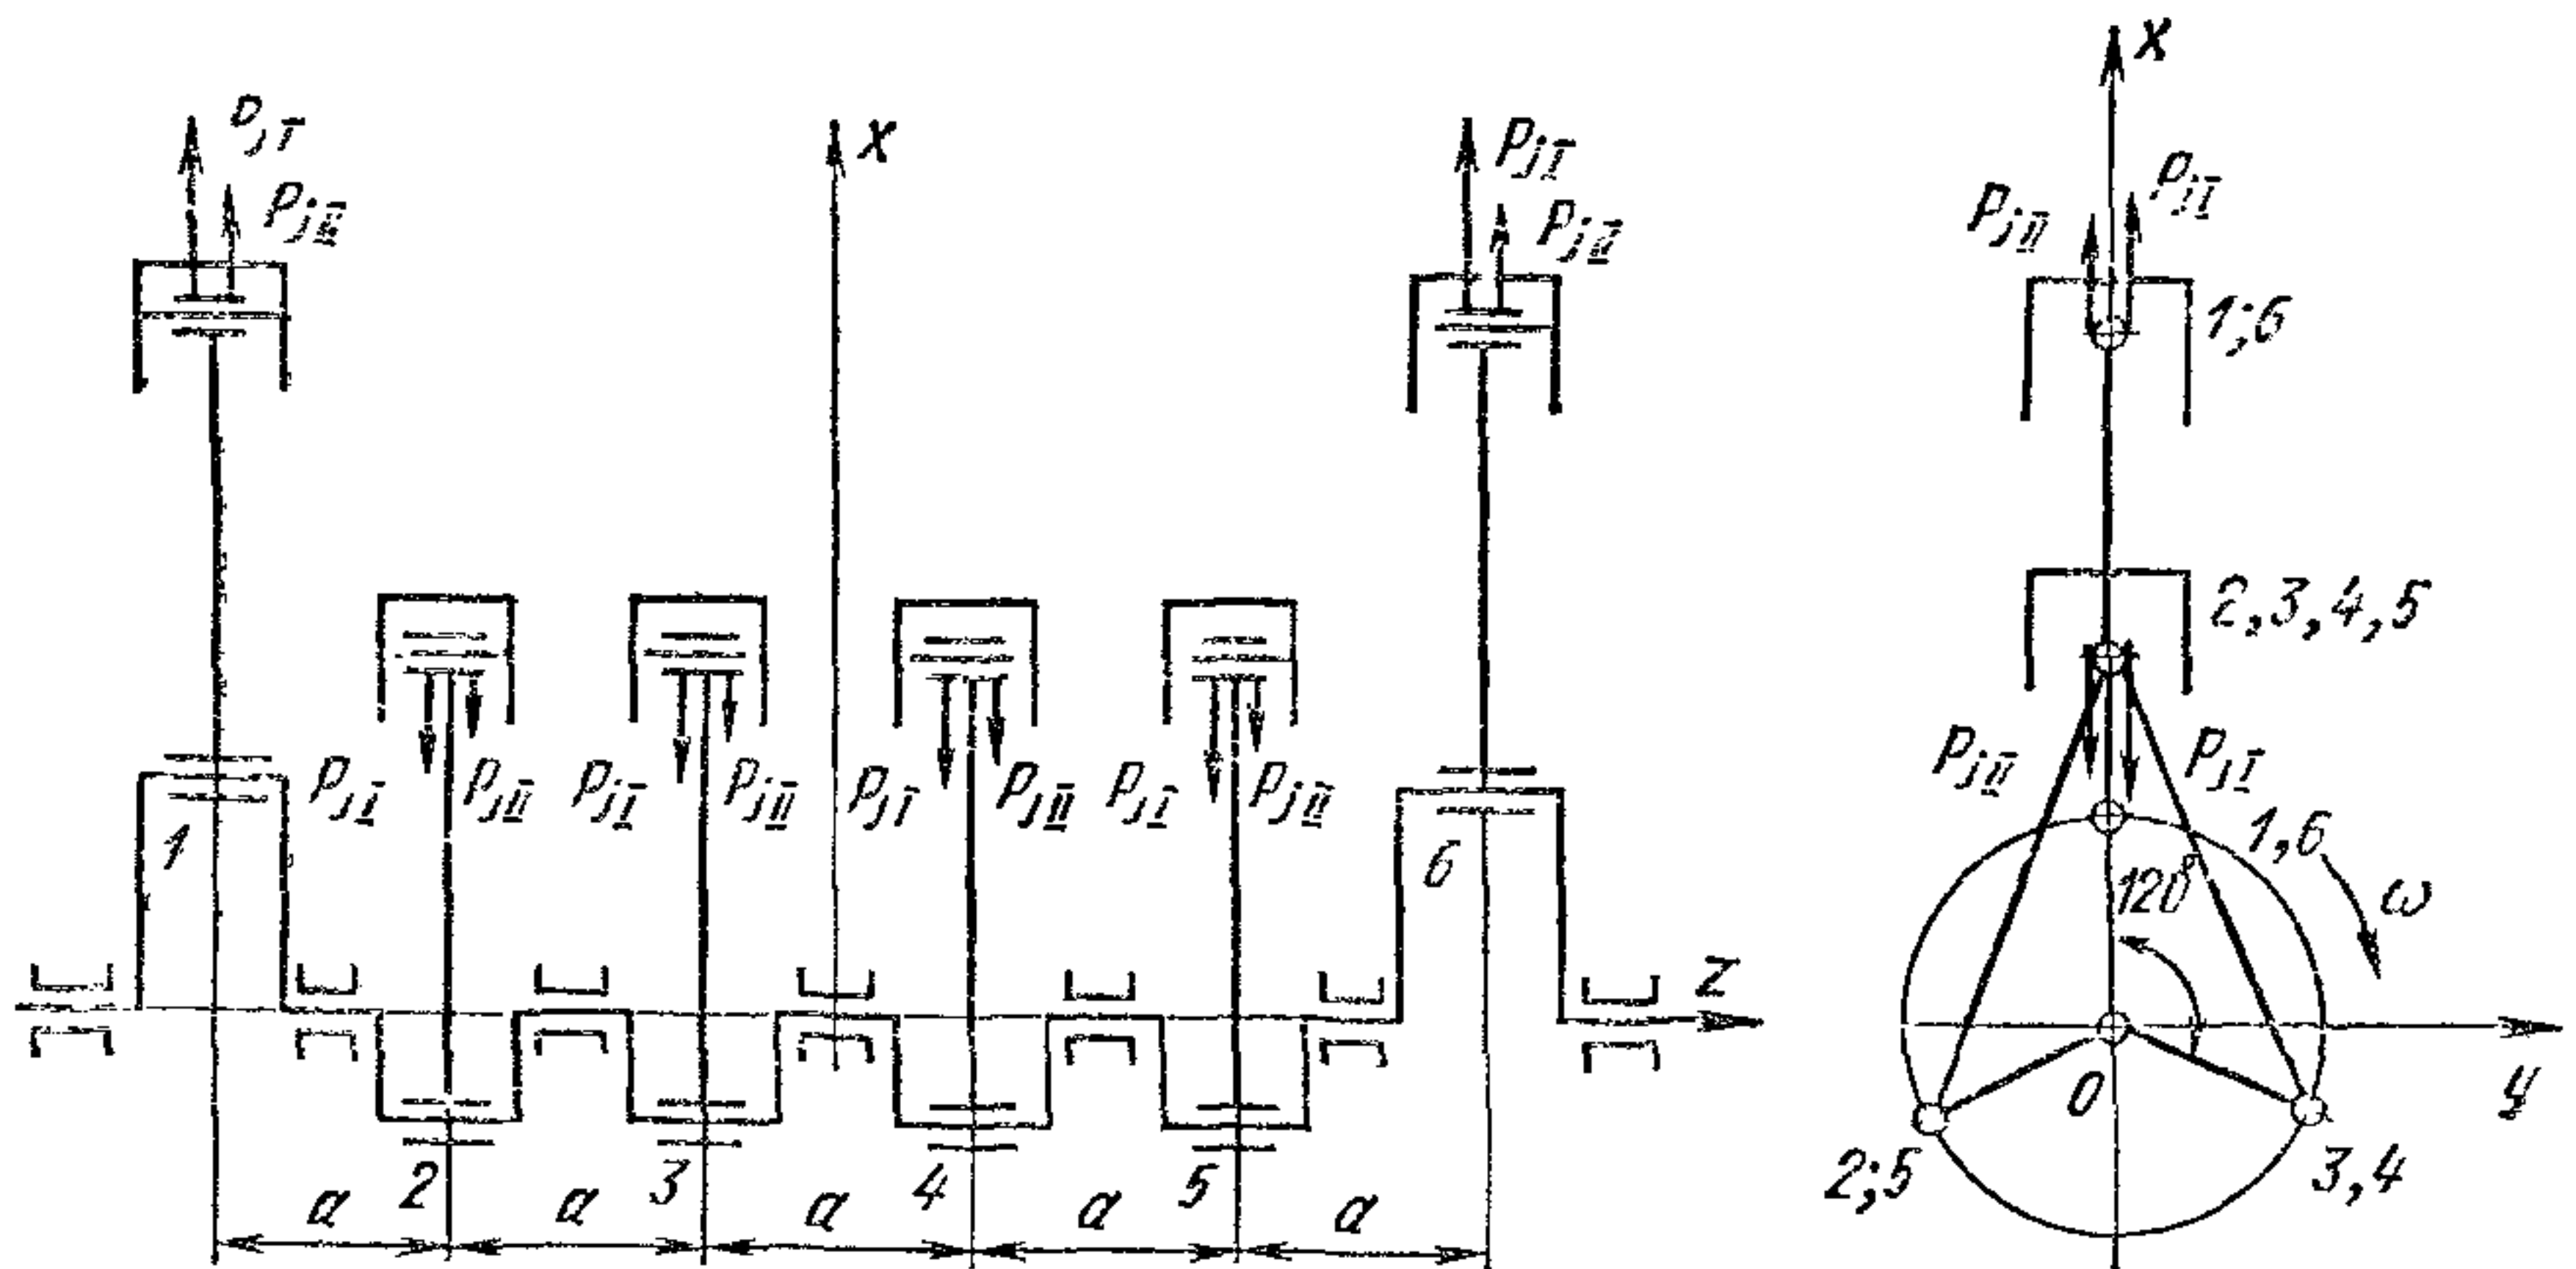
Схема однорядного шестицилиндрового четырехтактного двигателя
